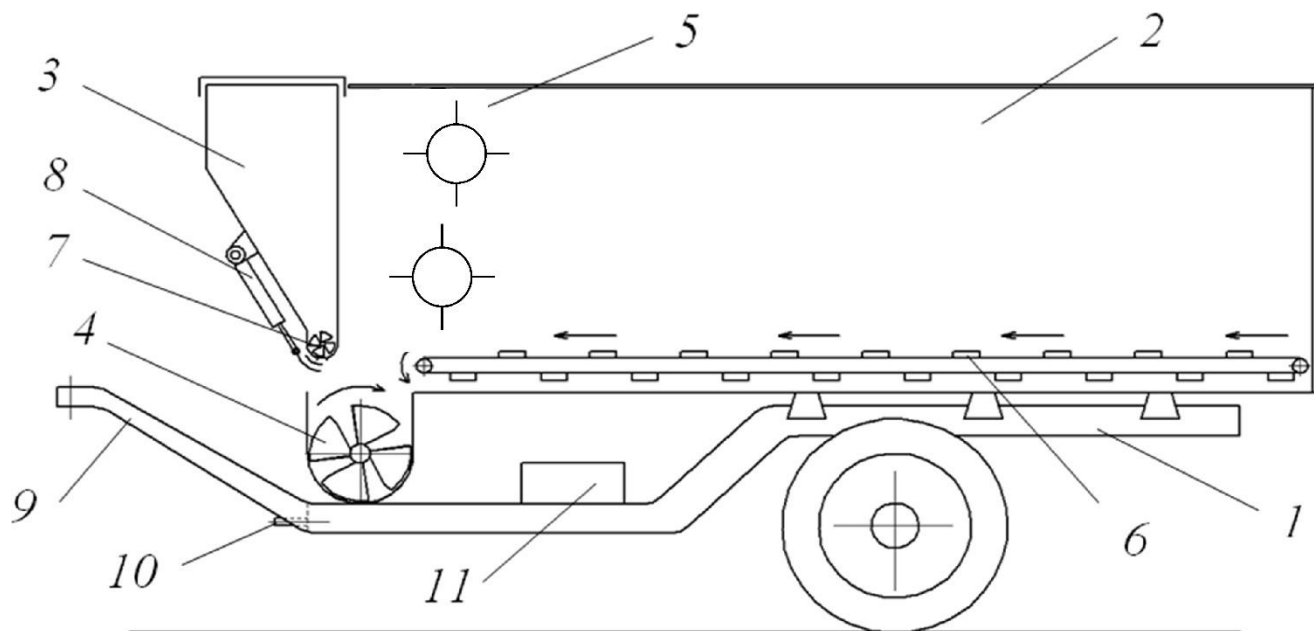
Конструктивно-технологічна схема змішувача-кормороздавача поточкового типу на базі КТУ-10: 1 – ходова частина з рамою; 2 – кузов; 3 – бункер-дозатор концкормів; 4 – лопатевий змішувач; 5 – бітерний кормовідділювач; 6 – позовжний транспортер; 7 – конвеєр-ворушилка; 8 – гідроциліндр; 9 – тягово-зчеплювальний пристрій; 10 – вал прийому потужності; 11 – редуктор
